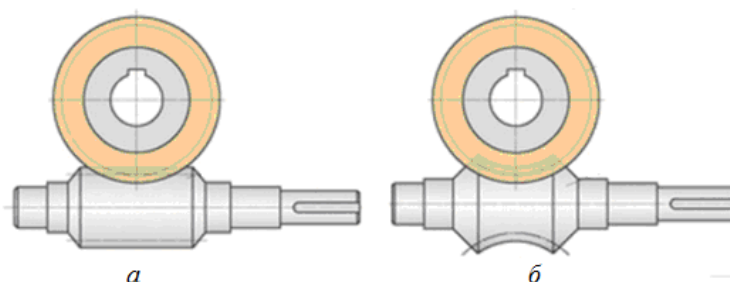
Типы червяков: *а* – цилиндрический; *б* – глобоидный
